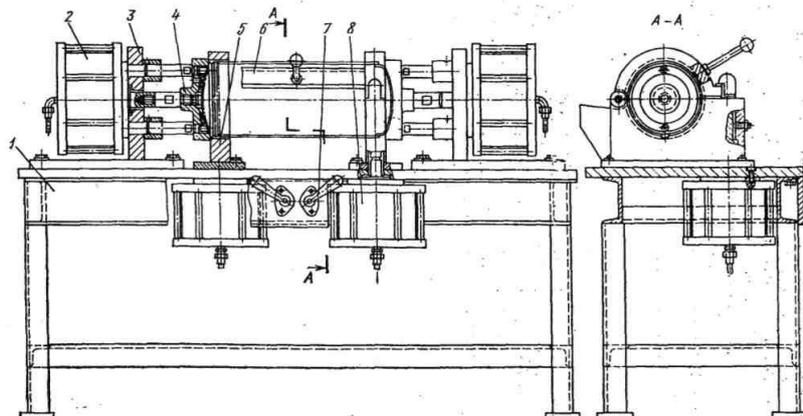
Установка для сборки небольших обечаяк с доньшками
